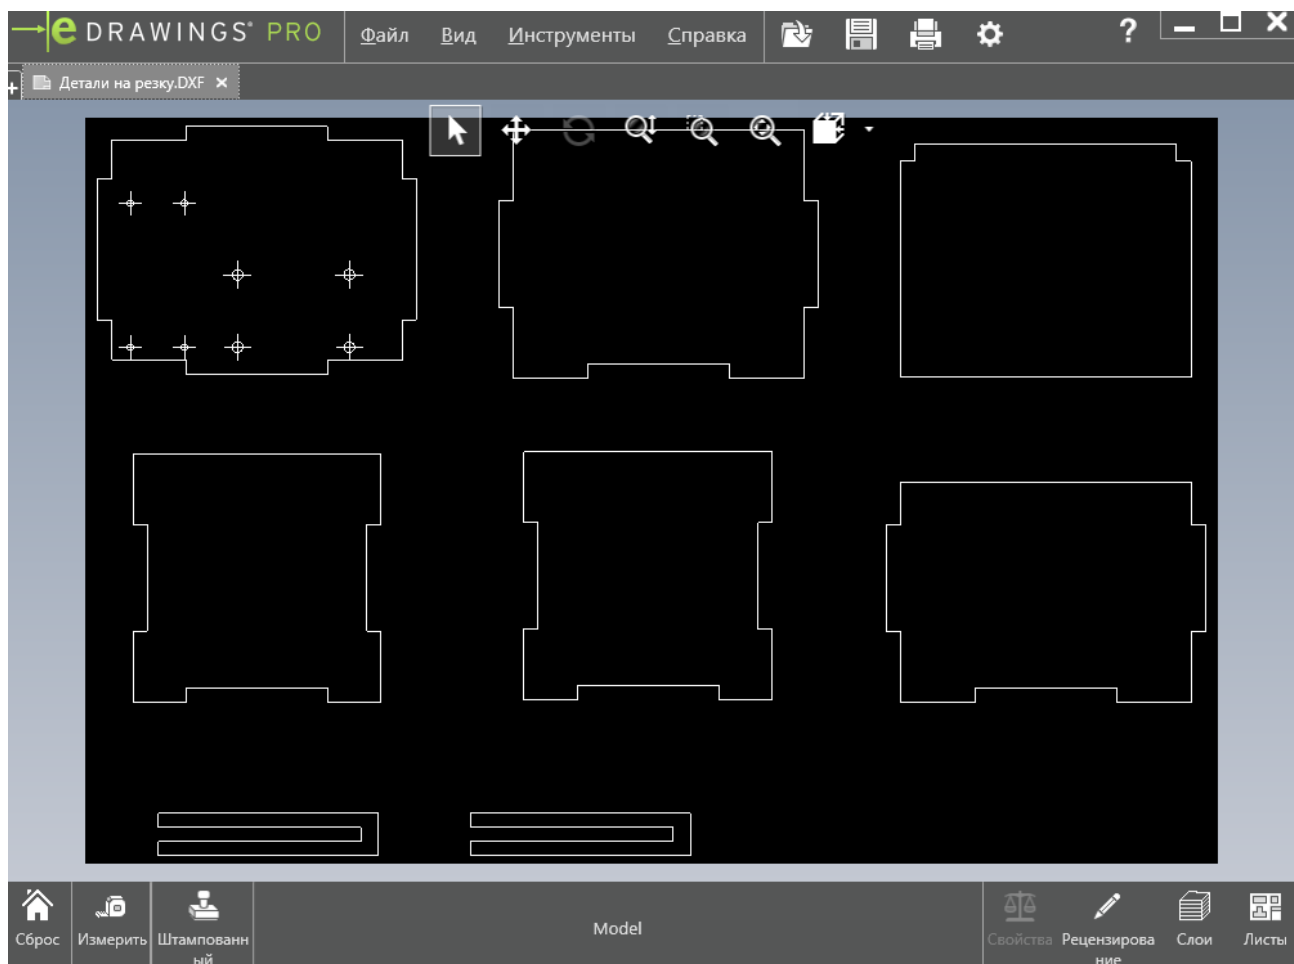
деталі конструкції в CAD форматі DXF
